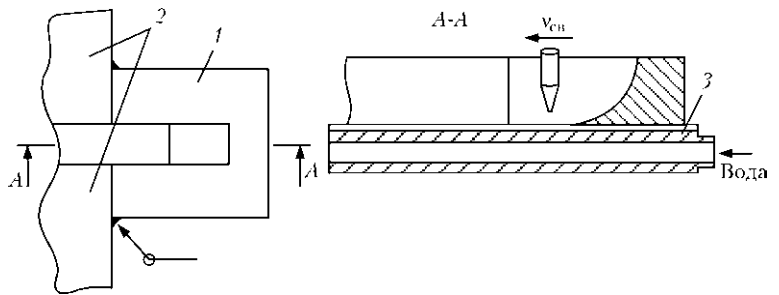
Схема выполнения сварки с выводной планкой: 1 — выводная планка; 2 — свариваемые плиты; 3 — формирующая подкладка
